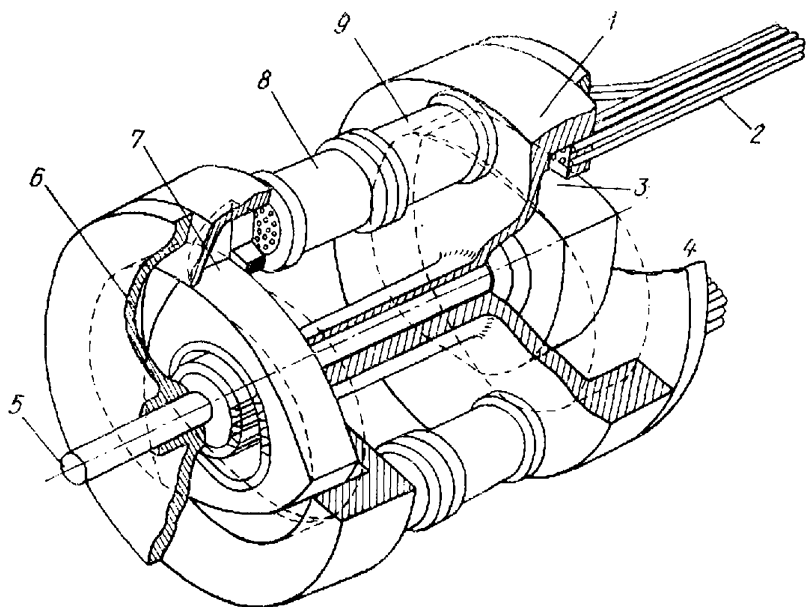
Схема Цвауера—Ванкеля роторного двигателя Стирлинга:
